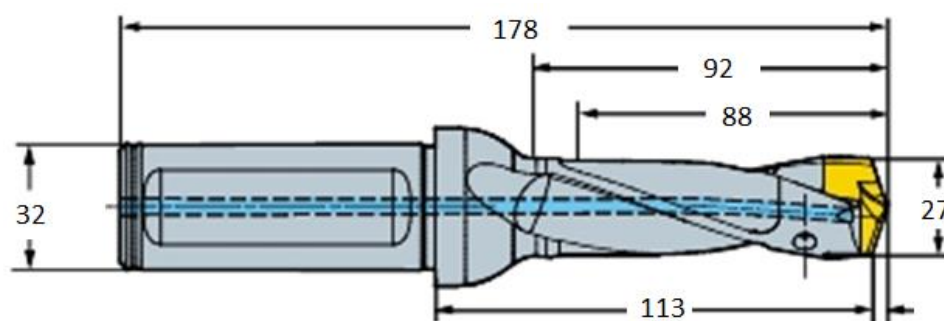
Сборное сверло Sandvik Coromant CoroDrill 870-2700-27L32-3
